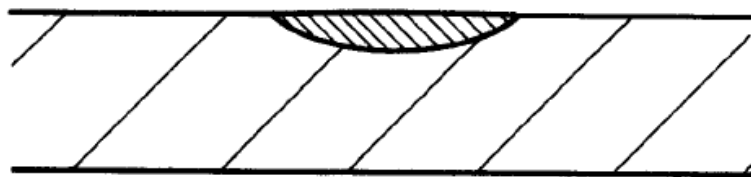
Penetración del cordón con soldadura TIG con corriente continua inversa. (Positivo en metal base (pieza) y negativo en el electrodo).
